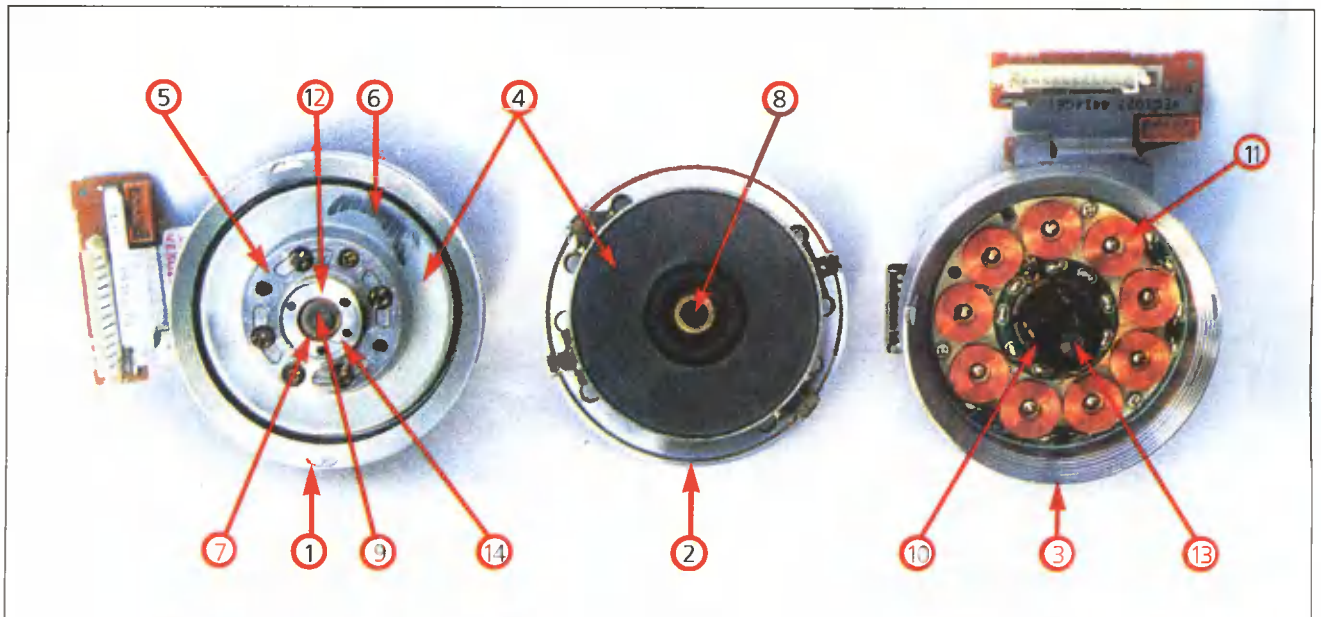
Блок видеоголовок: 1 — БВГ со снятым верхним цилиндром (ВЦ) (узел 1); 2 — верхний цилиндр с роторами ВТ и двигателя, вид снизу (узел 2); 3 — нижний цилиндр (узел 3); 4 — ротор ВТ; 5 — платформа ВЦ; 6 — идентификационная метка; 7 — фиксирующая шайба; 8 — подшипник скольжения; 9 — вал; 10 — статор ВТ; 11 — статор двигателя БВГ; 12 — платформа; 13 — торец вала; 14 — выемка платформы
